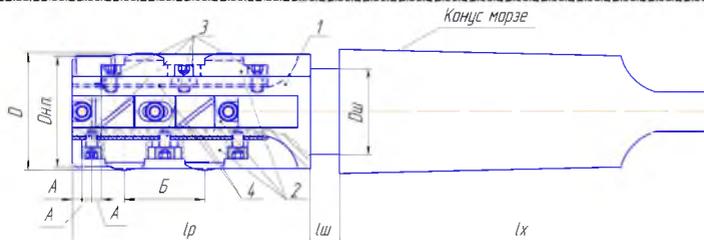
Общий вид сборной развёртки со сдвоенными безвершинными зубьями
